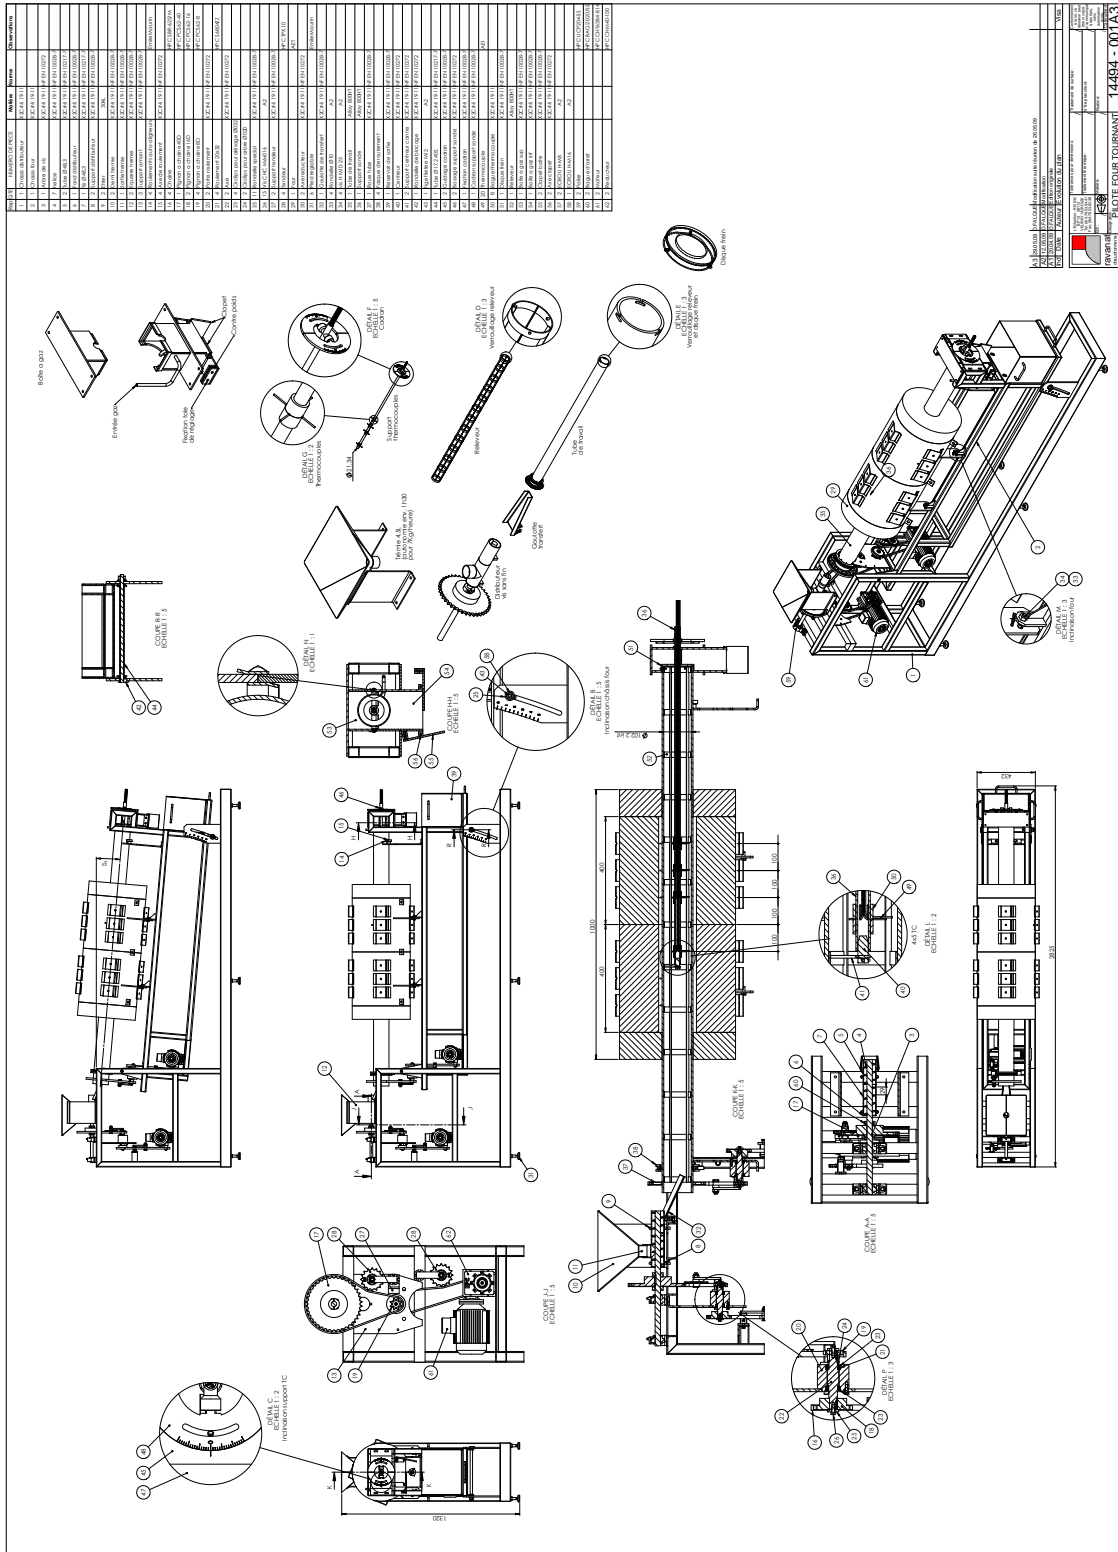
Plan détaillé du pilote de four tournant - imprimer en A3
